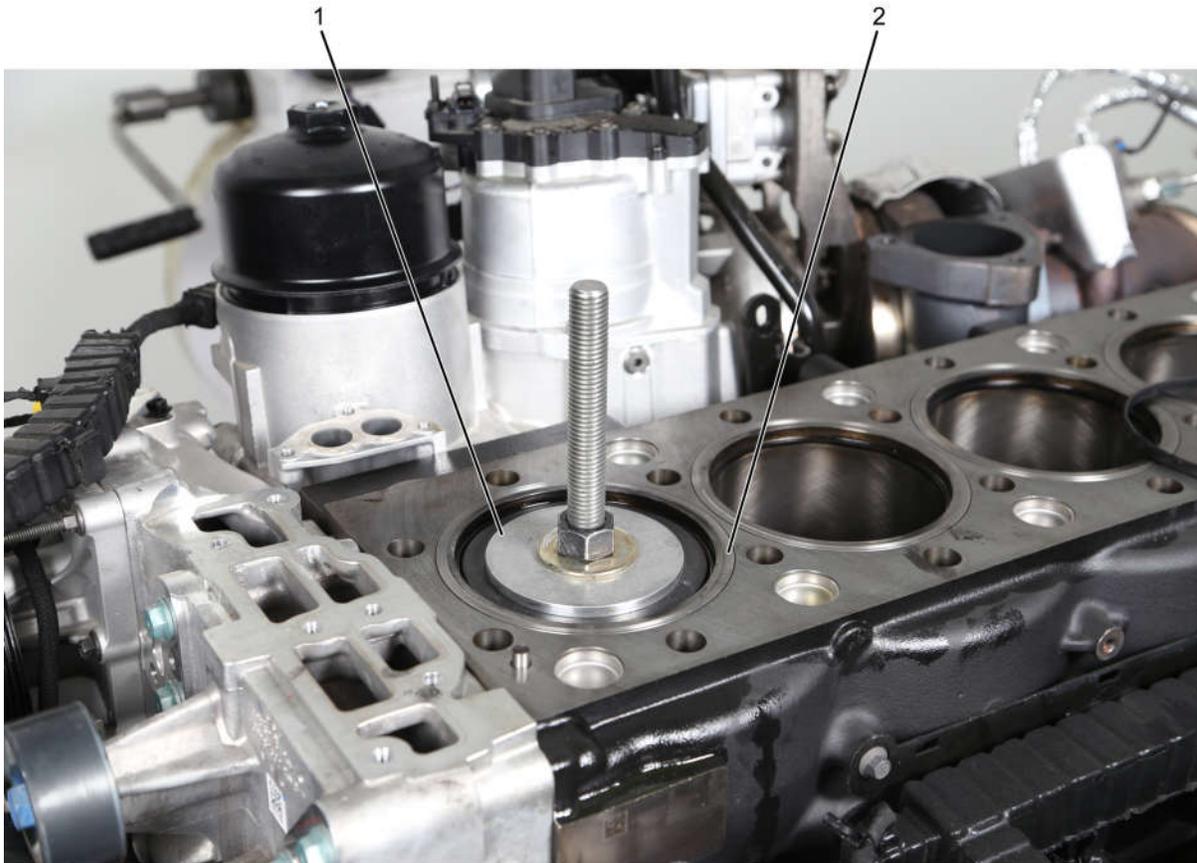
Kit extractor del conjunto de cilindro 12-192-01
